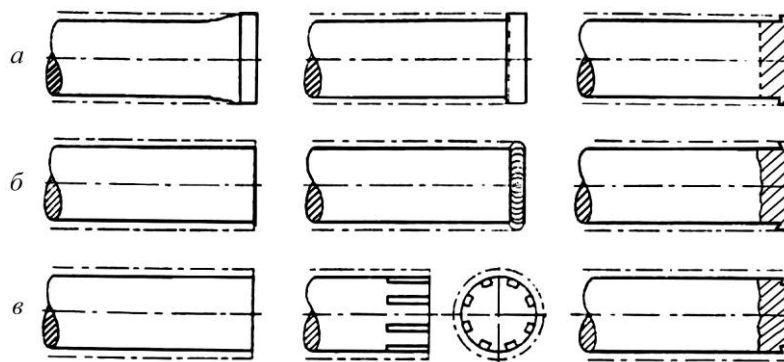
Способи механічної підготовки кінцівки гладкого вала під металізацію: *a* – токарна “підрізка” типу “ластів’ячий хвіст”; *б* – наплавлення і підрізання; *в* – фрезерування ривчаків або торцеве підрізання.
